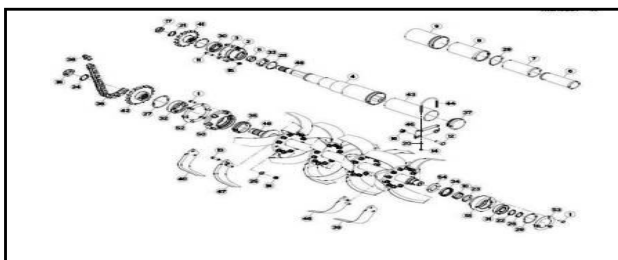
Vista explodida do rotor para o posto de trabalho 5851
